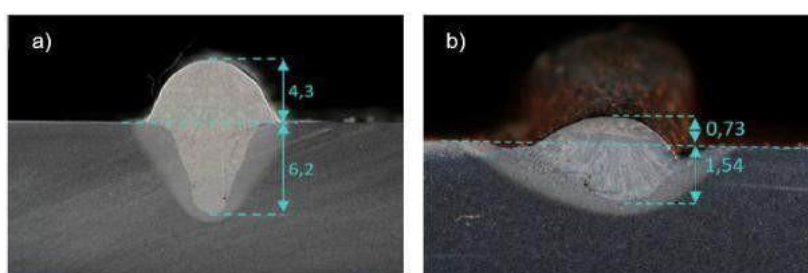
Macrografias. Fonte: O autor. Em a) Cordão de solda C1, $V_c = 0,6$ m/min; b) Cordão de solda C20, $V_s = 2,5$ m/min.
